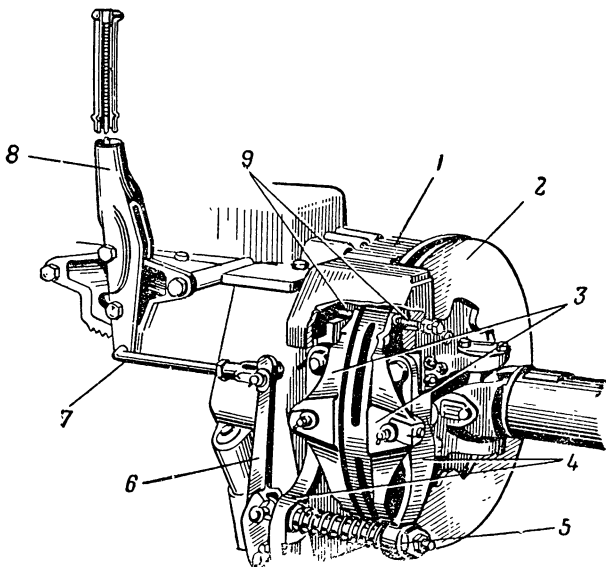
Центральный (ручной) дисковый тормоз и привод управления центральным тормозом автомобиля ГАЗ-51:
